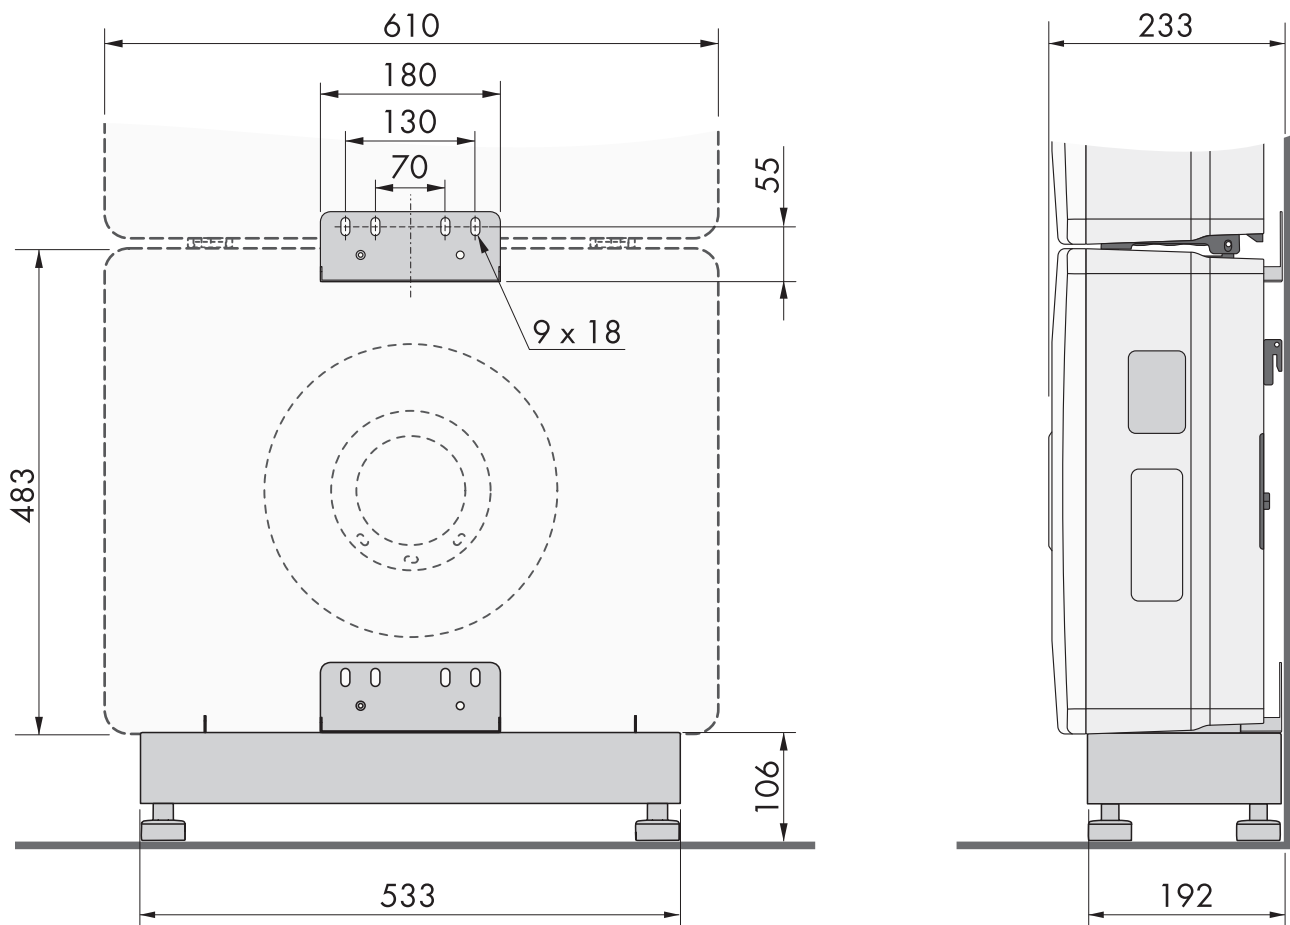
Posizione dei punti di fissaggio (misure in mm)
